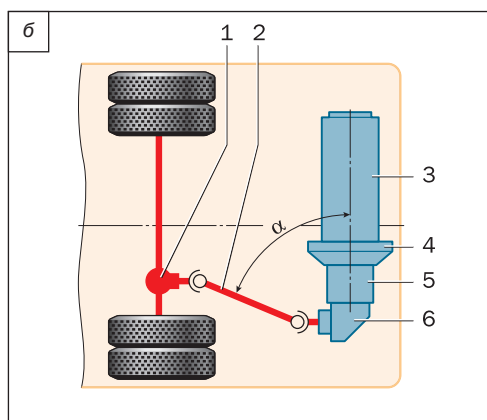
Заднеприводная заднемоторная компоновка с поперечным расположением двигателя и углом β равным 60° или 65° (а), 80° (б) и 90° (в): 1 — главная передача; 2 — карданная передача; 3 — двигатель; 4 — сцепление; 5 — коробка передач; 6 — угловой редуктор
